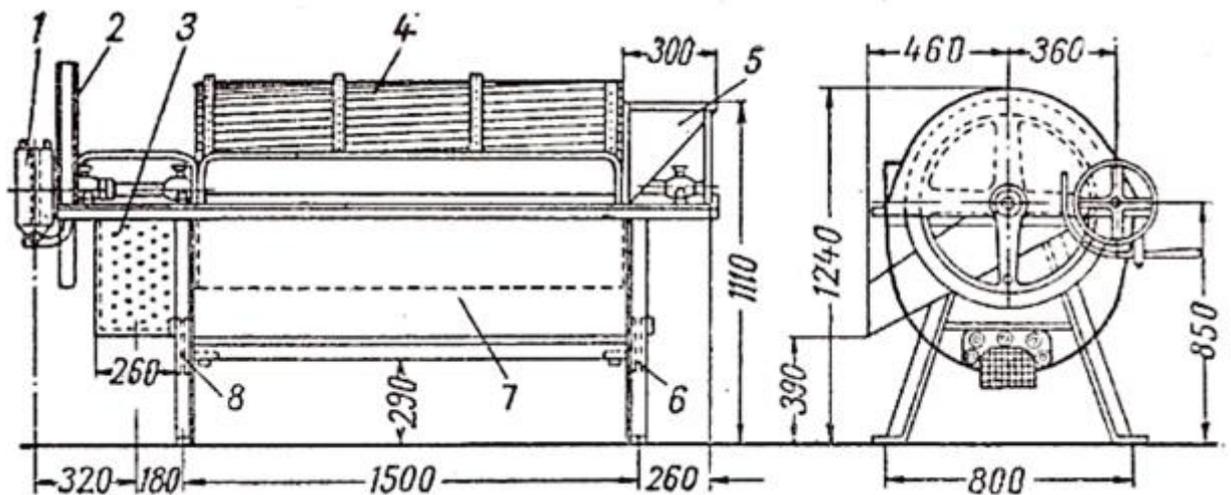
Схема барабанної мийки безперервної дії: 1 – робочий і холостий шків; 2 – передавальний механізм; 3 – випускний лоток; 4 – мийний барабан; 5 – завантажувальний лоток; 6, 8 – грязьові люки; 7 – корито для води.
